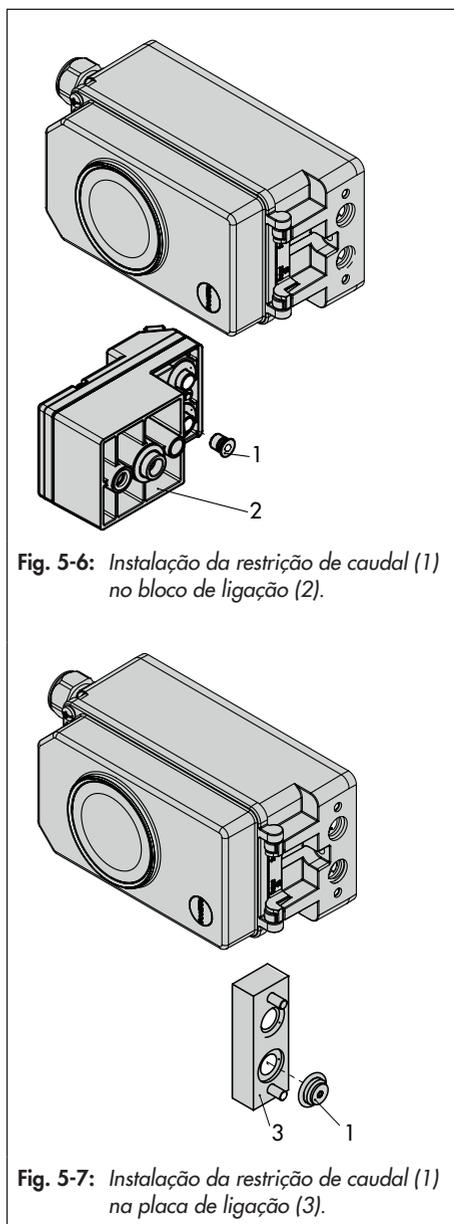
Instalação da restrição de caudal (1) no bloco de ligação (2).
